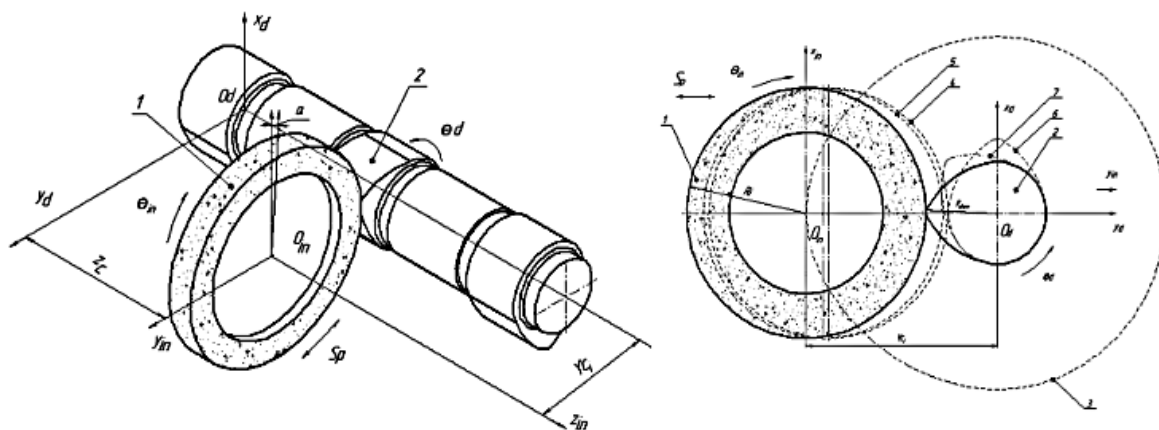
Схема шліфування кулачка розподільчого вала фірмою Junker
